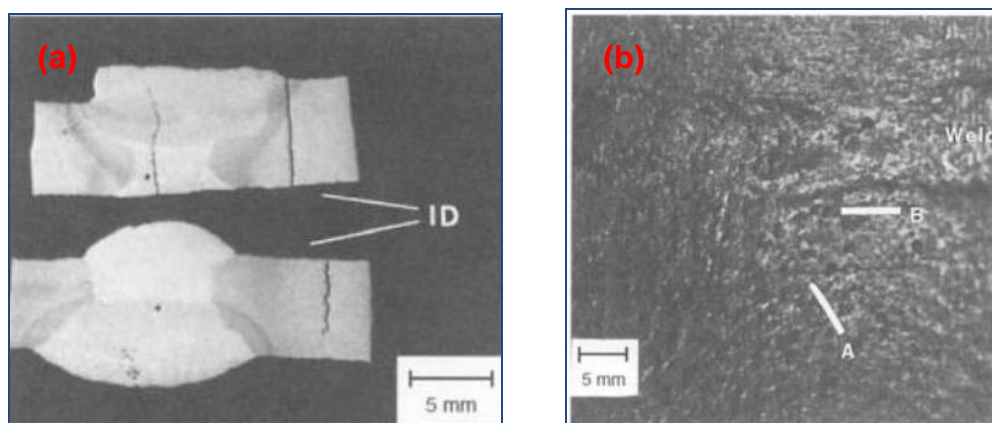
Se pudo observar a) Grietas originadas en la ZAC y b) cerca de la zona afectada por el calor. [16]
